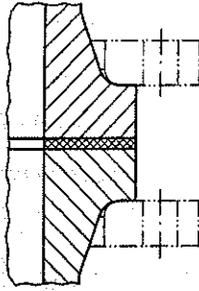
Vorschweißbund mit durchgehender Dichtung
